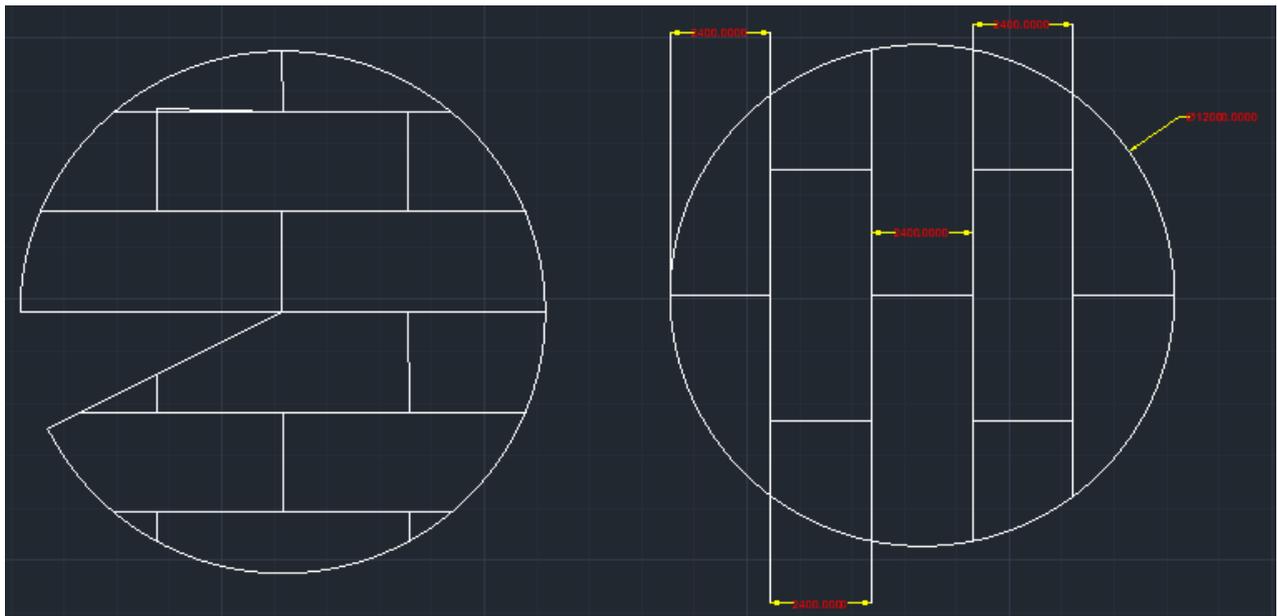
Mapa de la soldadura de la base y techo de un tanque sin la mejora
